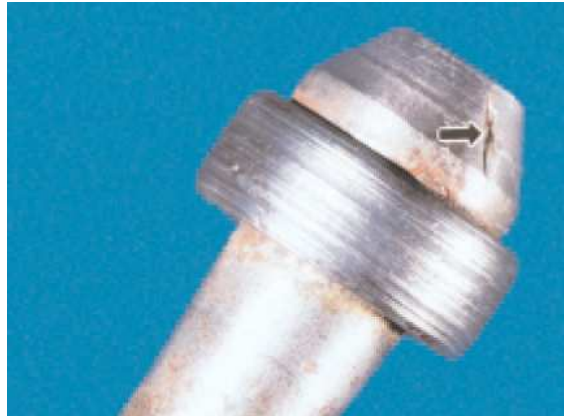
Casquillo de tubería de combustible rayado
